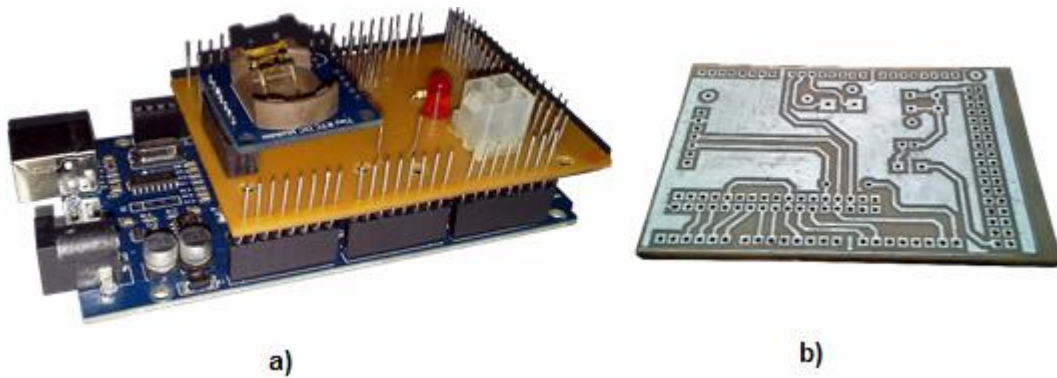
Tarjeta escudo: a) acoplado al Arduino, b) parte inferior sin ningún elemento soldado.
